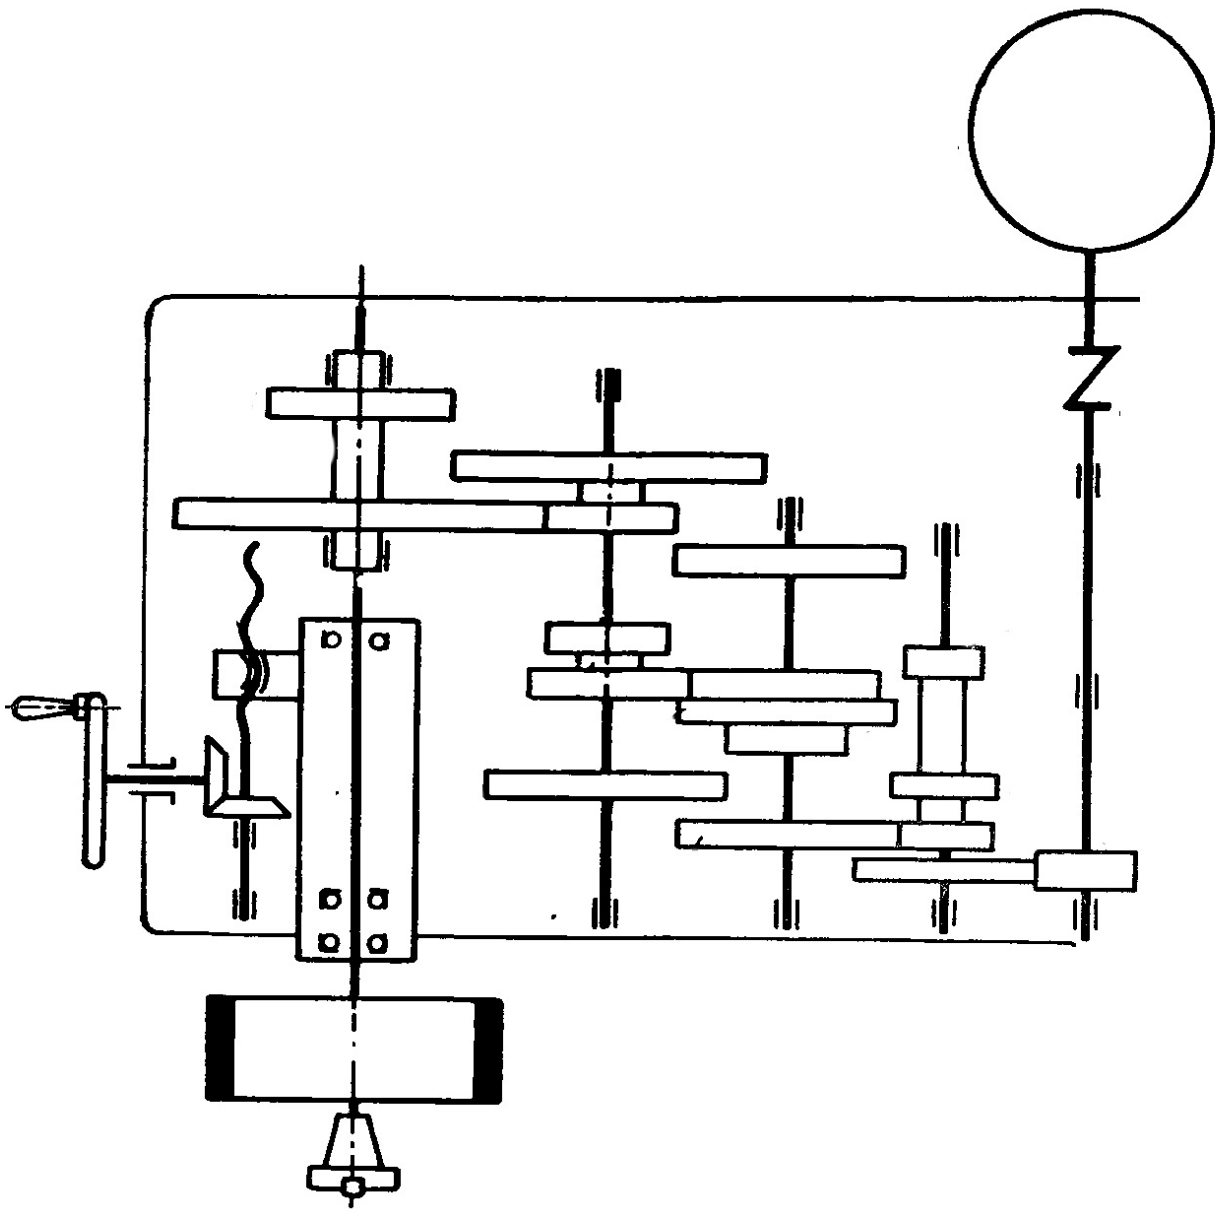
Німа кінематична схеми коробки швидкостей фрезерного верстата
